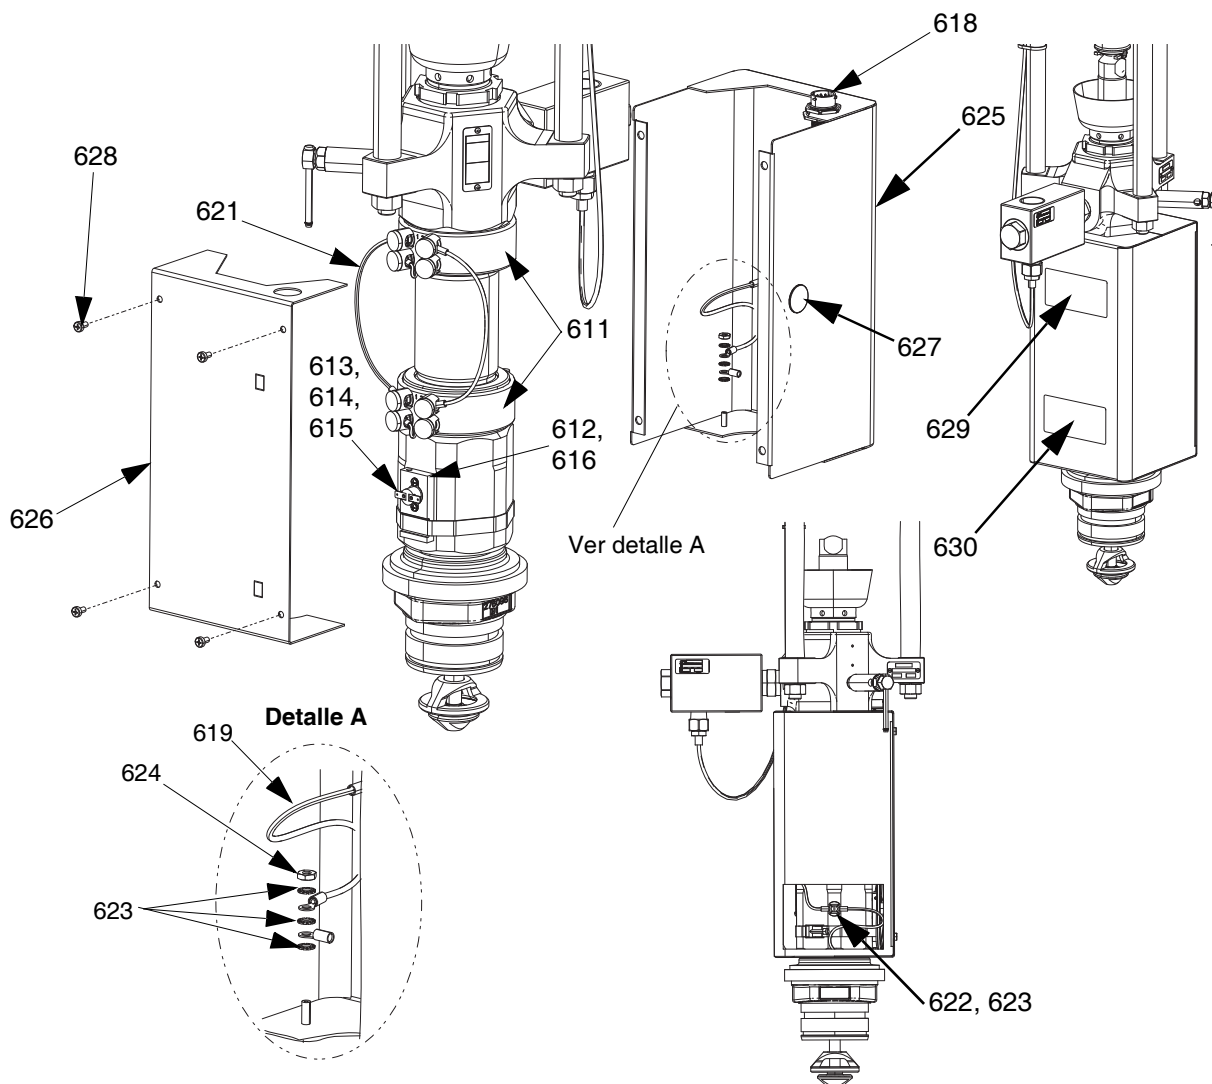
Kit de calentador de bomba Check-Mate 200 CS, 25R450
